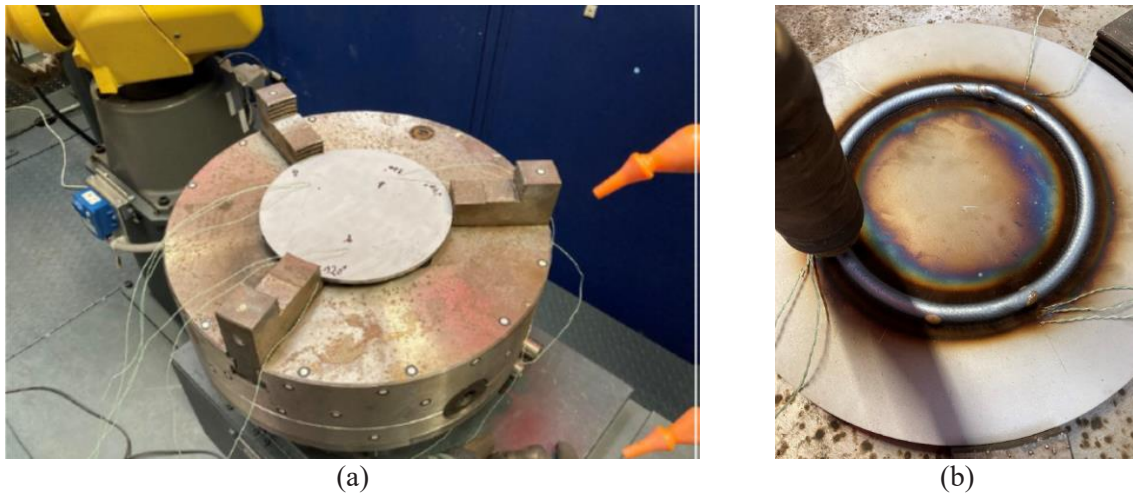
Cellule de fabrication additive arc fil de la plateforme AFH du CETIM : a) vue d'ensemble du dispositif avant fabrication, b) vue du tube en cours de fabrication.
